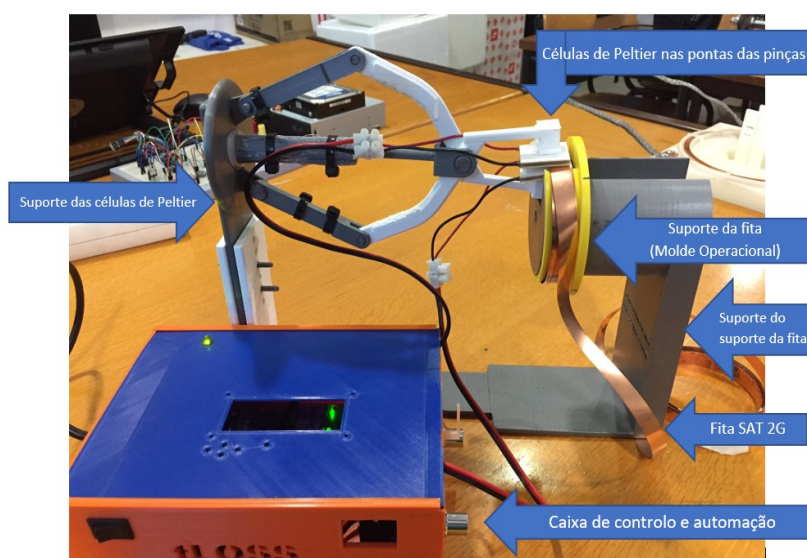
Configuração e composição da máquina de solda em conjunto com o molde operacional impresso
